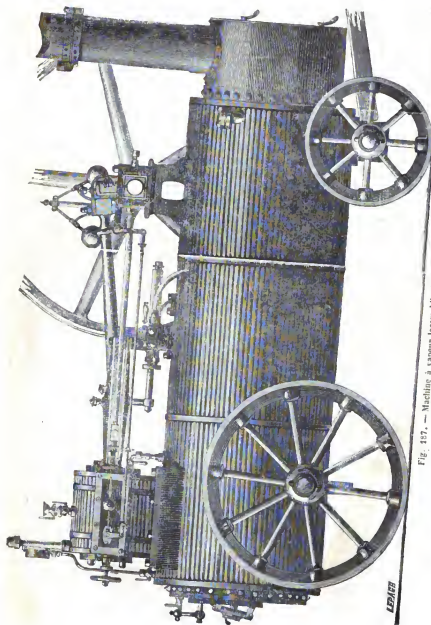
Machine à vapeur locomobile de M. Cumming, à Orléans.
